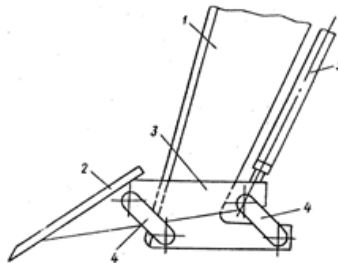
Рабочий шарнирно – соединенный орган рыхлителя
